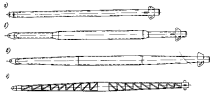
Типы судовых стрел: а — цилиндрическая; б — ступенчатая цилиндрическая; в — цилиндрическая с коническими участками; г — ферменная.
